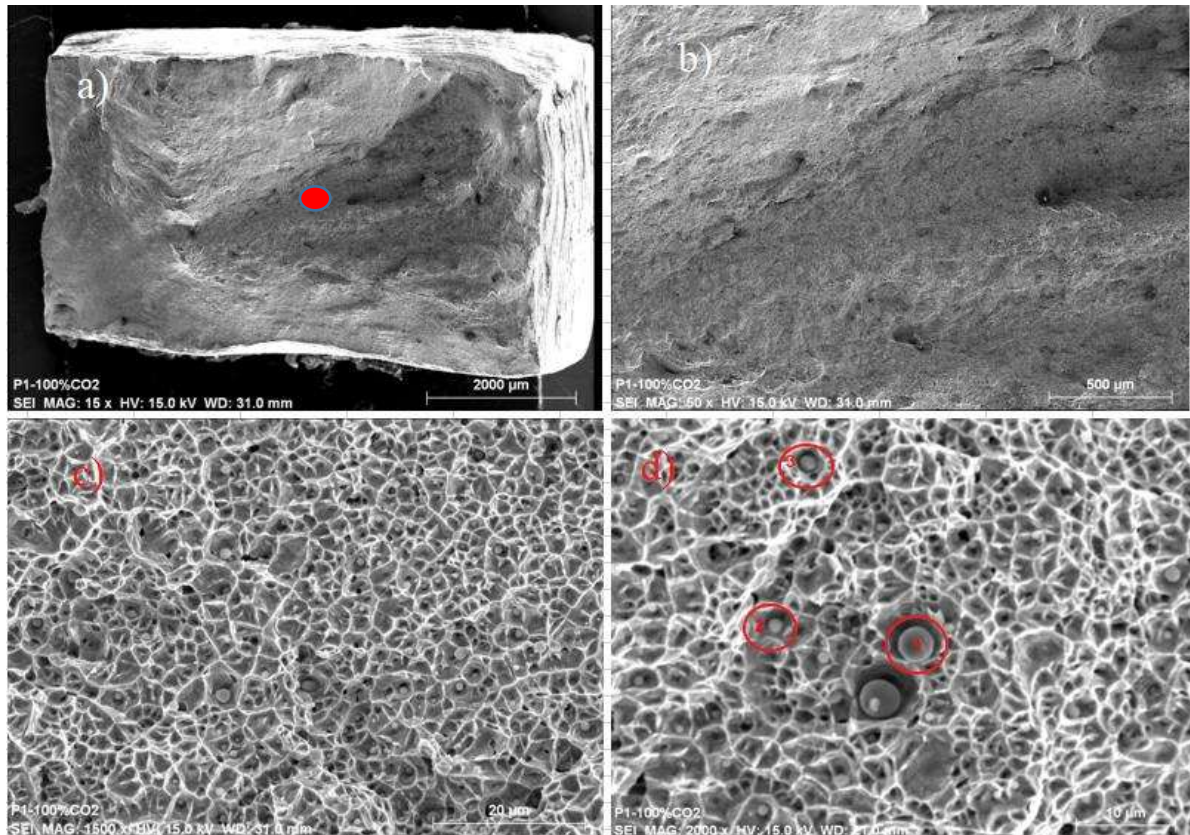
Imágenes de la superficie de fractura de la probeta soldada con 100% CO₂.
